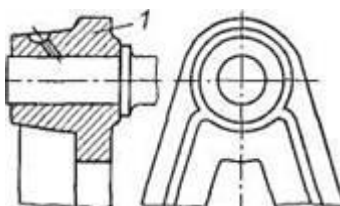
Неразъемный подшипник скольжения: 1 — станина
